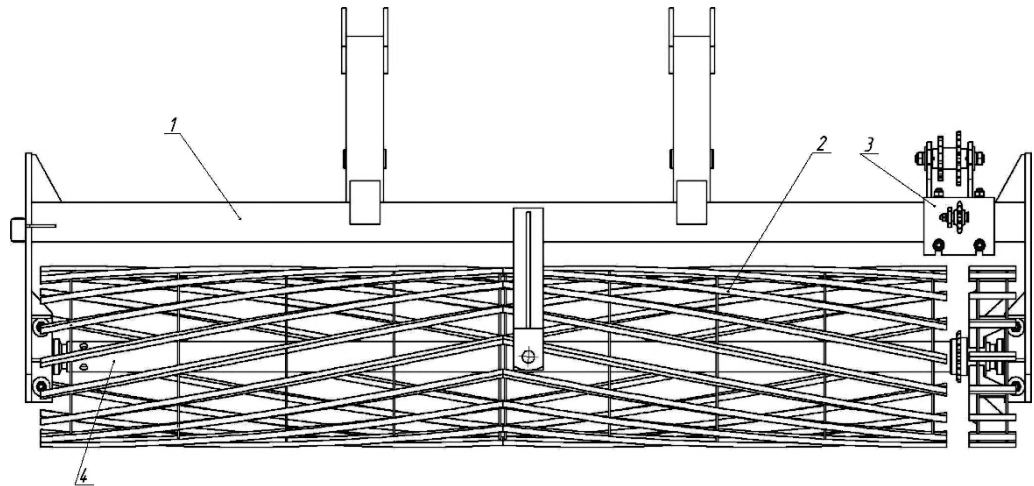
Прикочуючий привідний каток: 1 - рама; 2 - струна, 3 - блок зірочок; 4 - вал.
